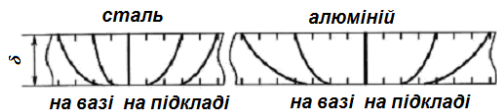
Регламентовані перерізи зварних швів під час зварювання в інертних газах: максимально допустима товщина основного металу під час зварювання на базі не більше 4 мм
